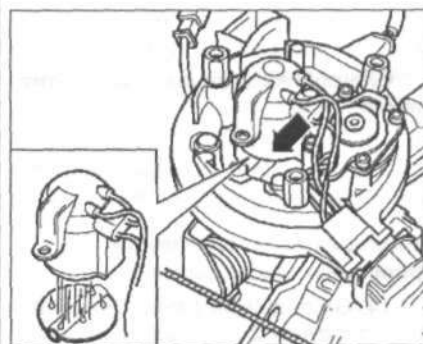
Заведите двигатель и оставьте его работать на холостых оборотах или, если двигатель не заводится, прокрутите коленчатый вал стартером. Должен произойти процесс впрыска топлива форсункой.
